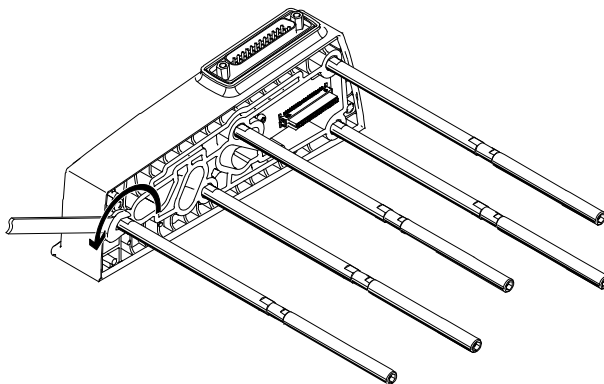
Entfernen der Gewindestangen von der linken Endplatte
